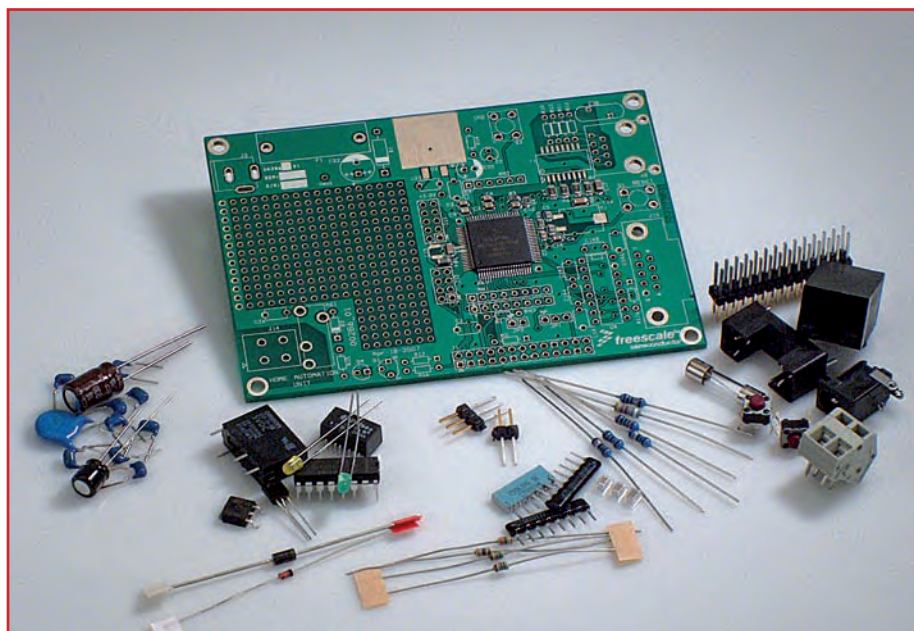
El kit DigiButler listo para ser ensamblado, completo y con la placa con los componentes SMD ya montados. El proyecto supone una hora de trabajo cuidadoso de soldadura. (El contenido del paquete no se muestra; las partes que se suministran en cada momento pueden ser diferentes de la que se muestra en la foto).
